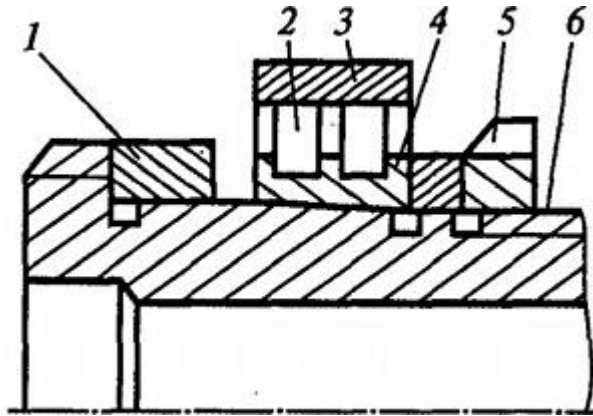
Схема регулирования предварительного натяга роликоподшипника серии 3182100: 1 — кольцо; 2 — ролики; 3 — наружное кольцо; 4 — внутреннее кольцо; 5 — гайка; 6 — шпиндель
